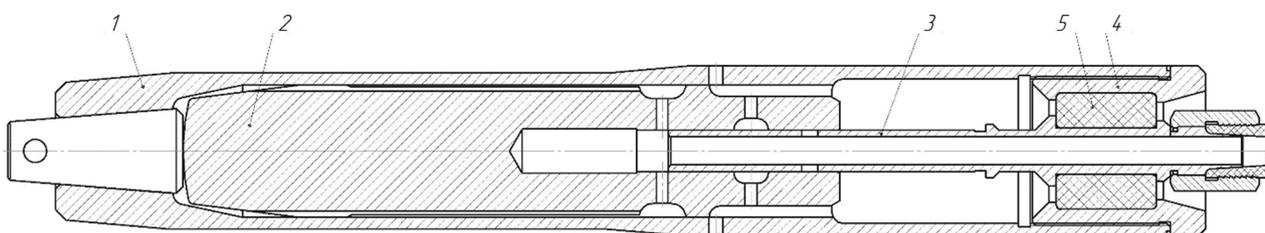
Общий вид экспериментального образца пневмоударного механизма с тремя рабочими камерами: 1 – корпус с наковальней; 2 – ударник; 3 – патрубок; 4 – гайка; 5 – амортизатор
